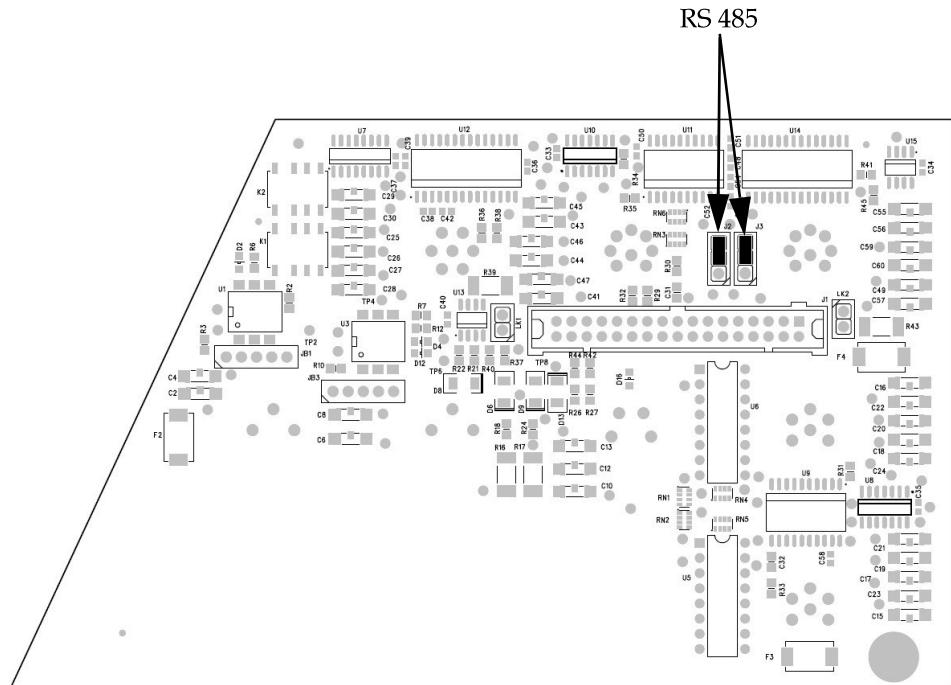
Configurações do jumper RS 485 (PCB 7)
